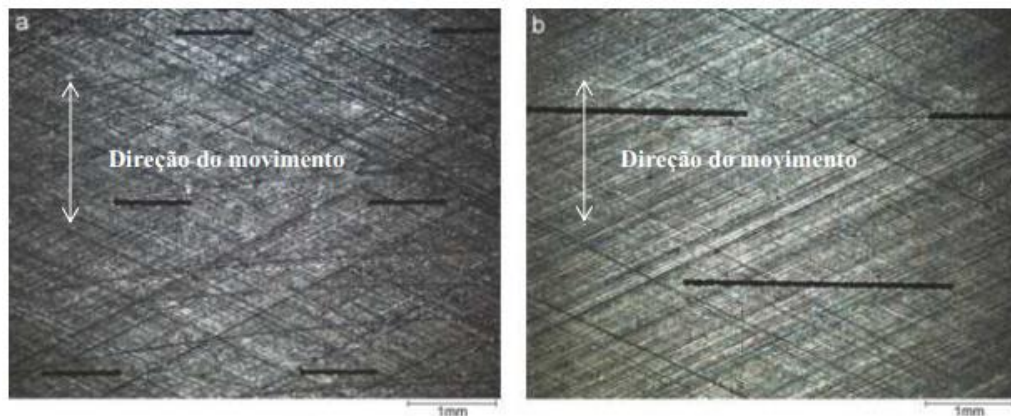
Perfil geométrico de aplicação por laser: a) 1mm b) 3mm
